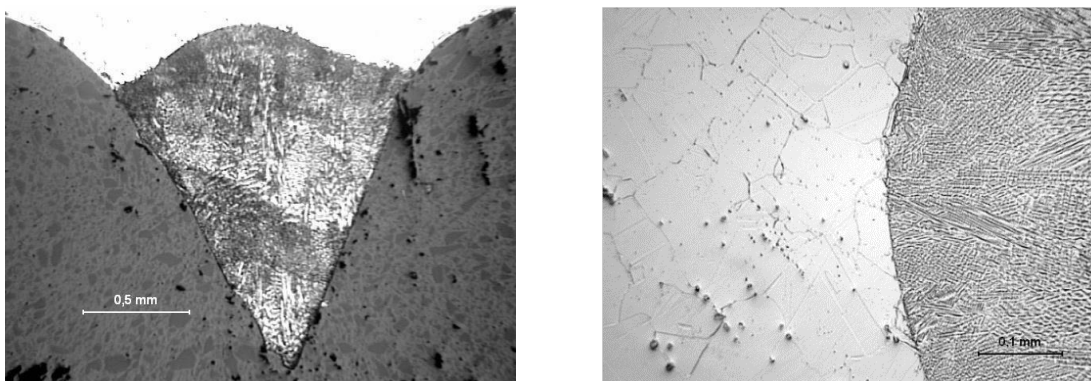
Cordón de soldadura en estado bruto. Se observa una estructura diferenciada entre el metal base (granos equiaxiales) y el material aportado (dendritas)
